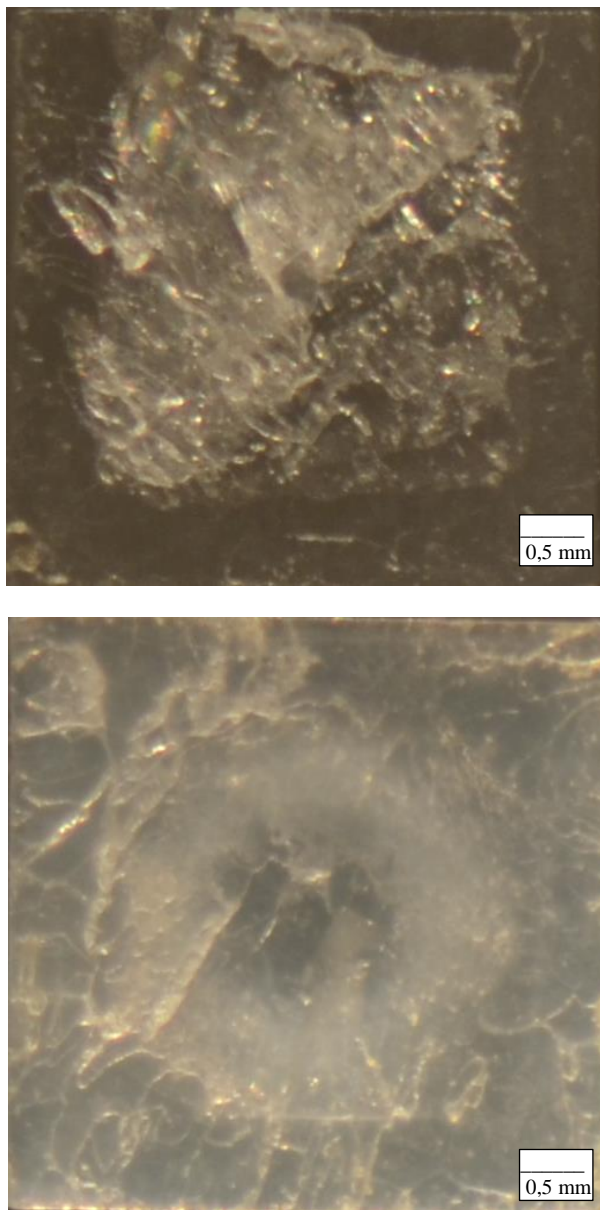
Aspecto da fratura dos corpos de prova injetados no inserto metálico, à temperatura de 190 °C e comprimento de fluxo 1, (a) com linha de solda e (b) sem linha de solda.
